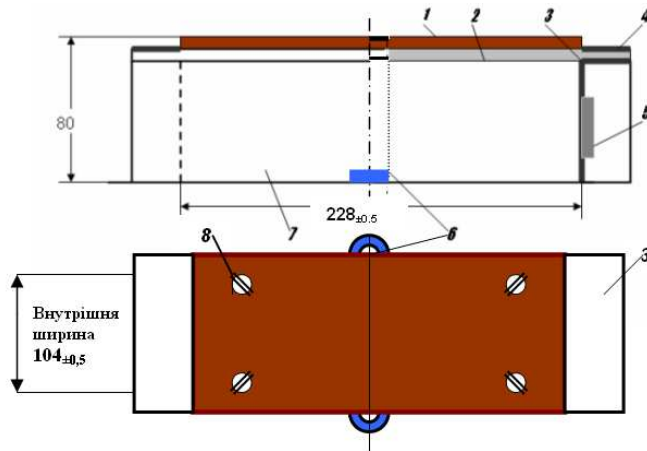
Ковпак ковзуна ТАУС^М — зварний варіант конструкції
